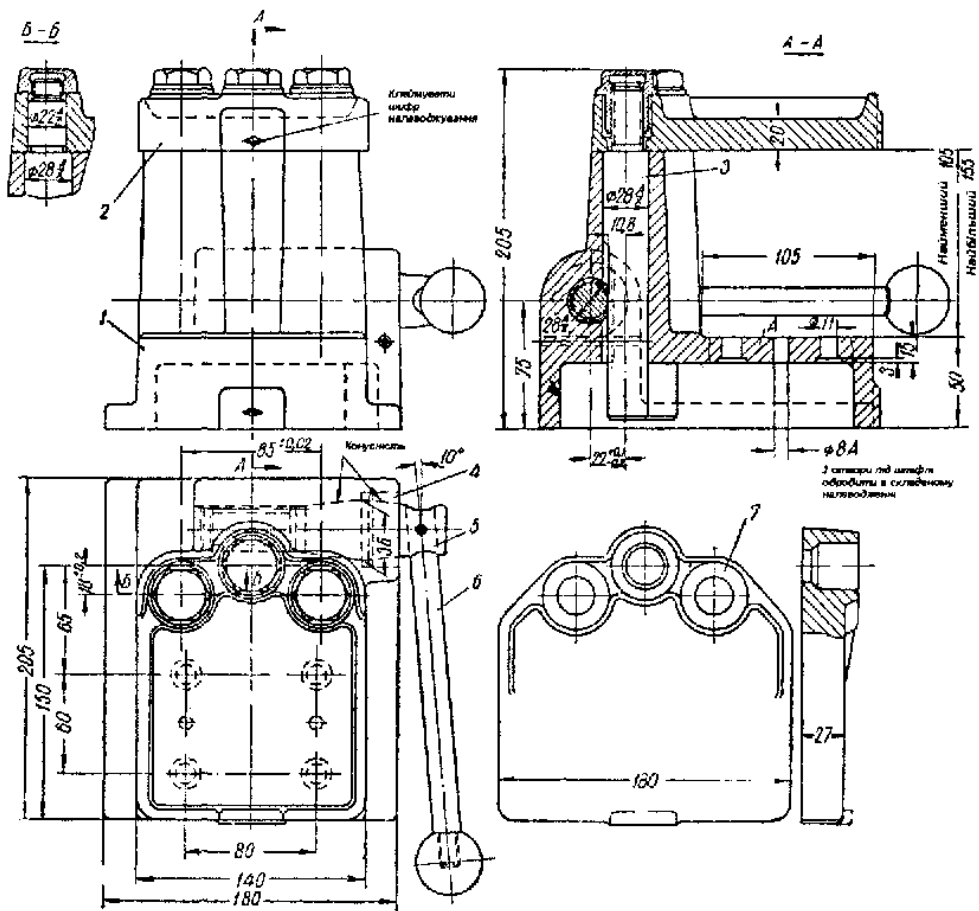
Консольний скальчастий кондуктор з рейково-конусним механізмом
